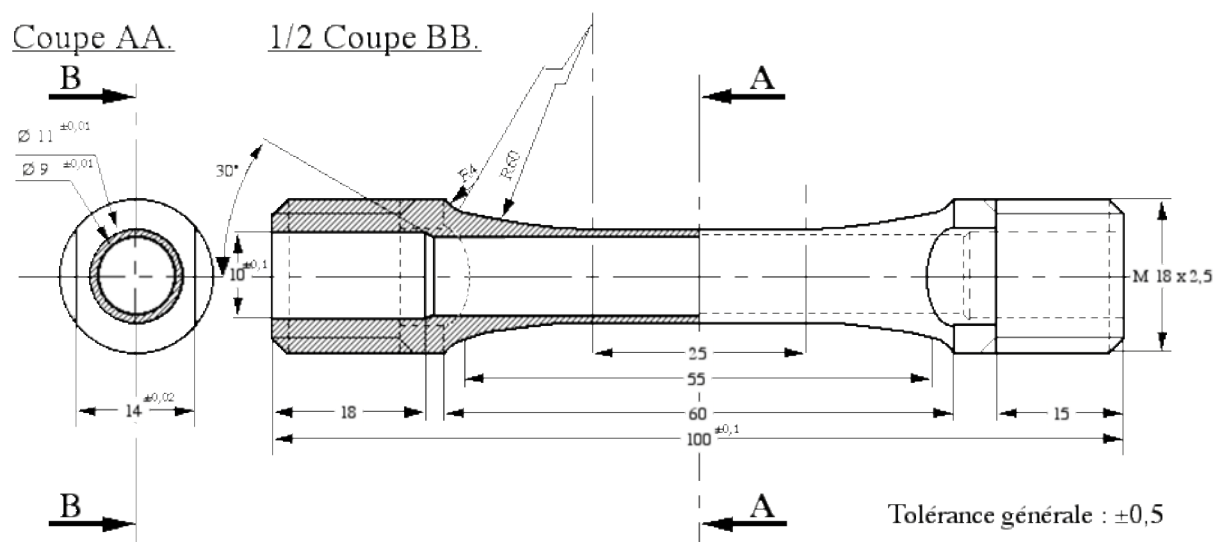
Schéma de l'éprouvette de fatigue mécano-thermique
